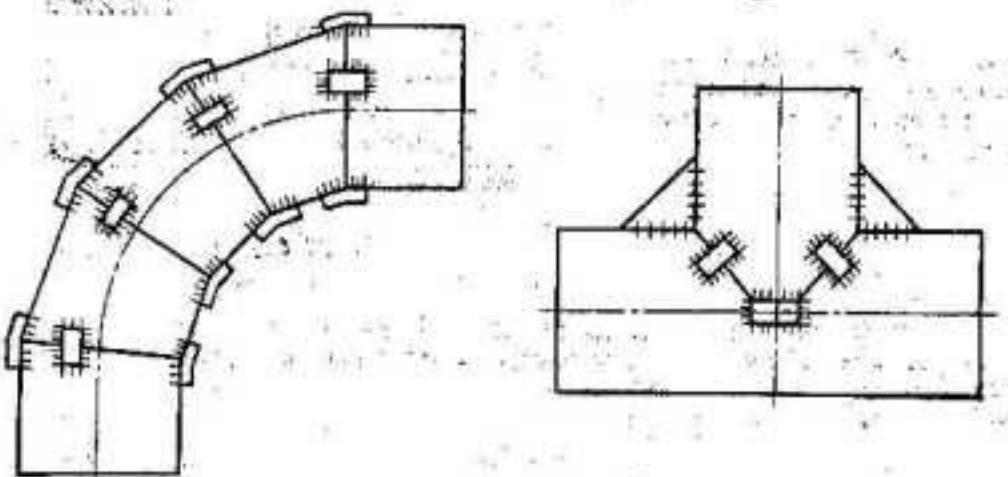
Усиление сварных фасонных деталей.
